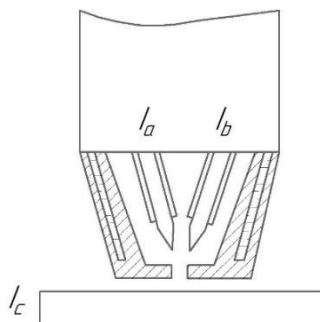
Схема плазменной сварки на обратной полярности
